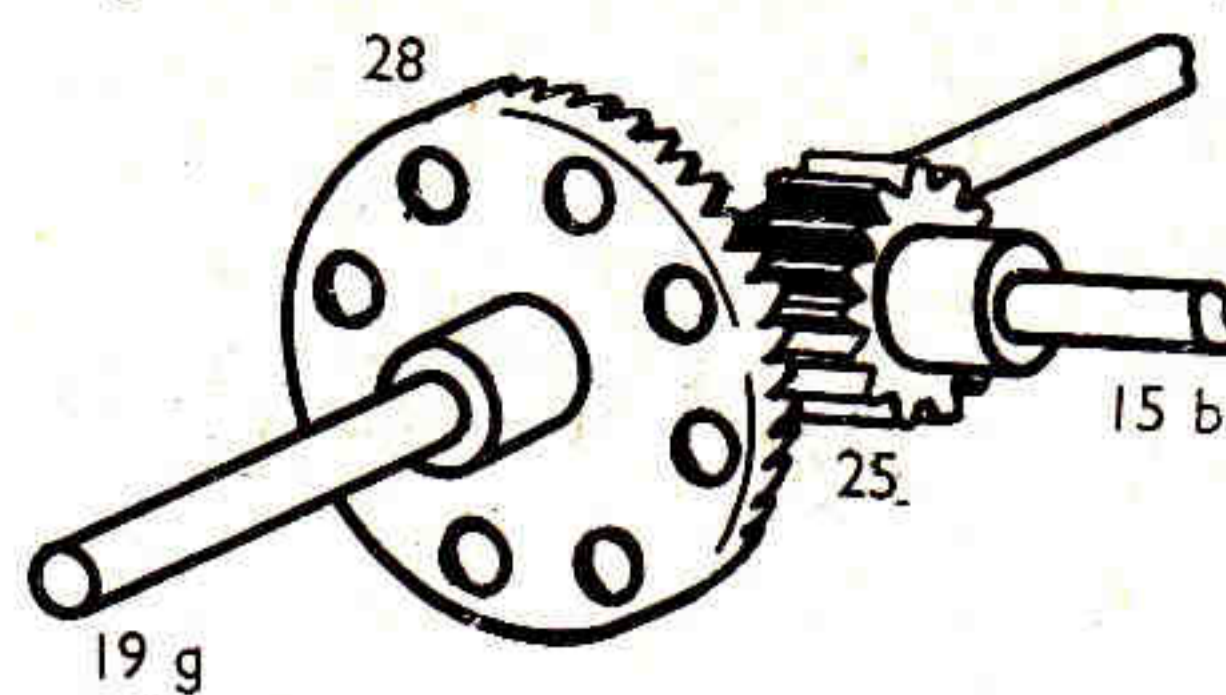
Position de deux engrenages placés sur des arbres perpendiculaires.
